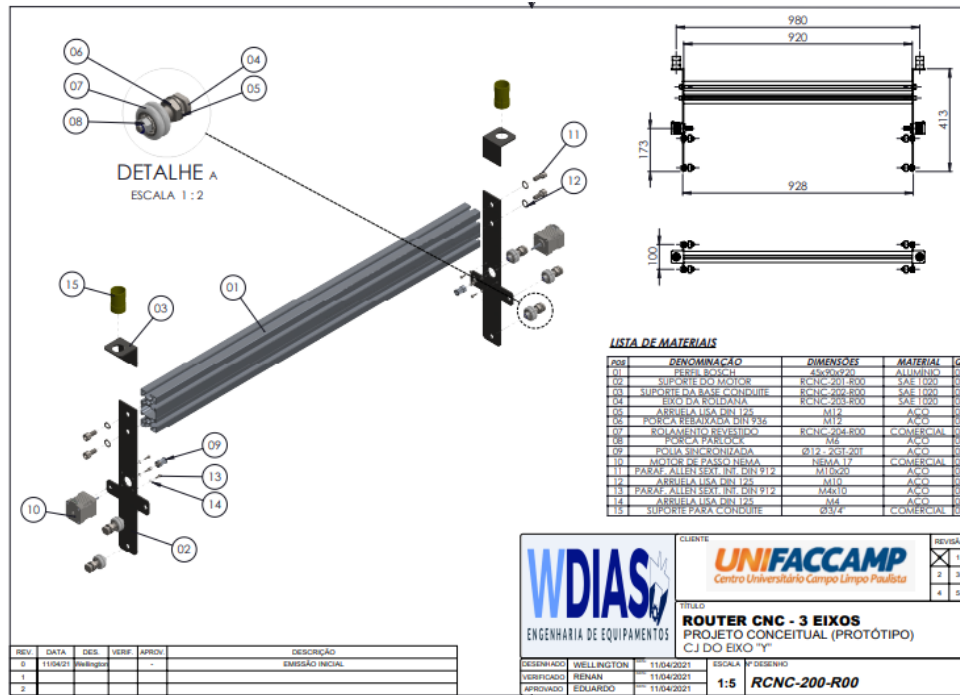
Desenho 2D da montagem do eixo "Y" – com descrição de componentes materiais.
